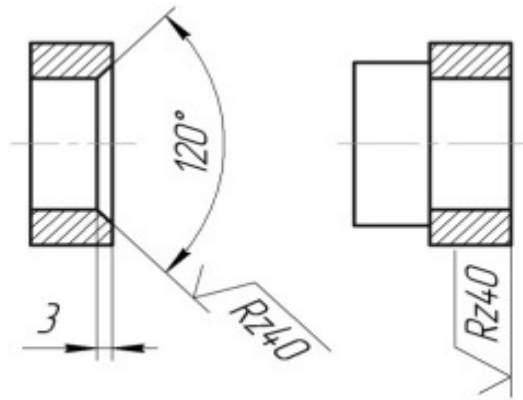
Оформление детали, ремонтируемой сваркой, наплавкой, нанесением металлопокрытий
